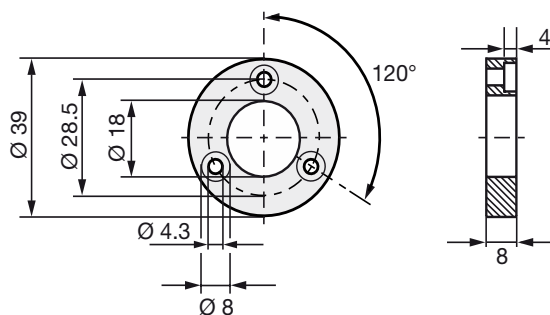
Positionsgeber BTL-P-1018-3R für hochdruckfesten Betrieb
